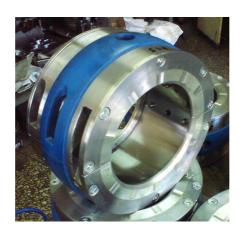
Подшипник электродвигателя ПДУ-120
